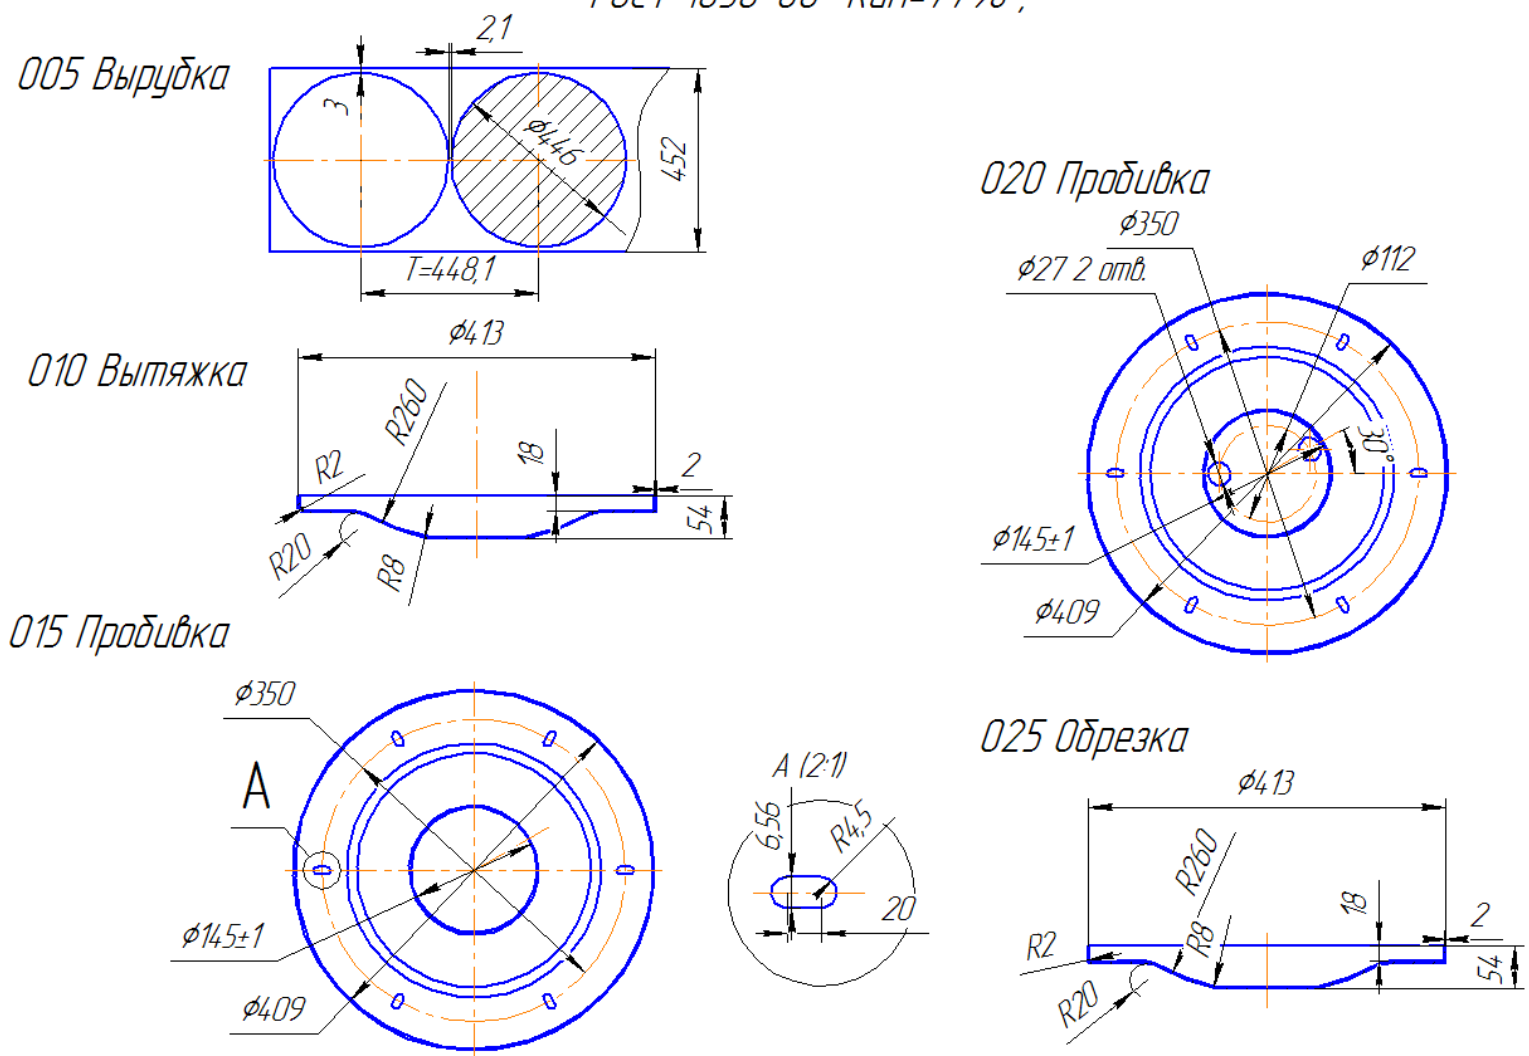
Варианты изготовления детали – «Упор»
